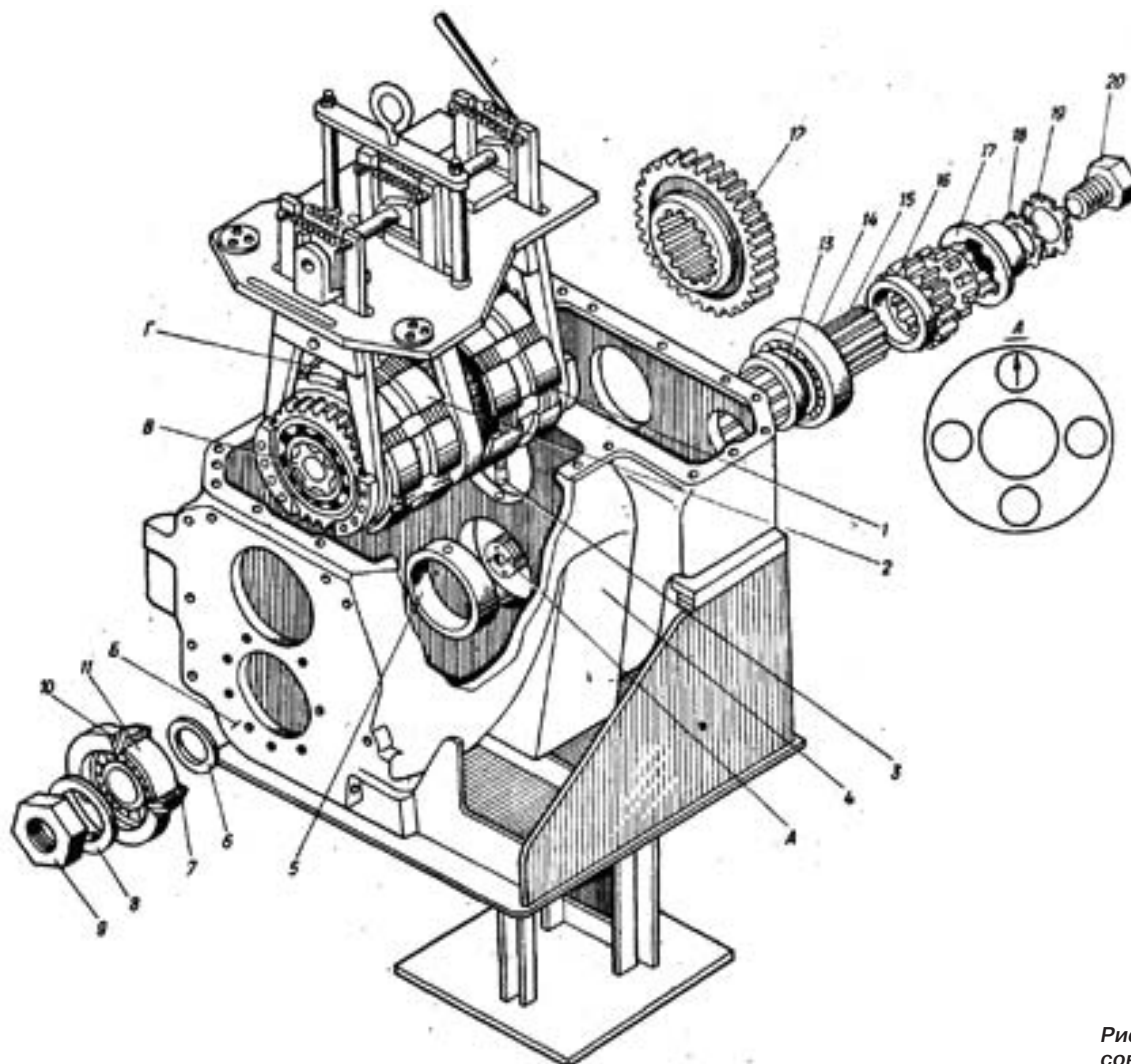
Установка вторичного вала и гидроподжимных муфт:
